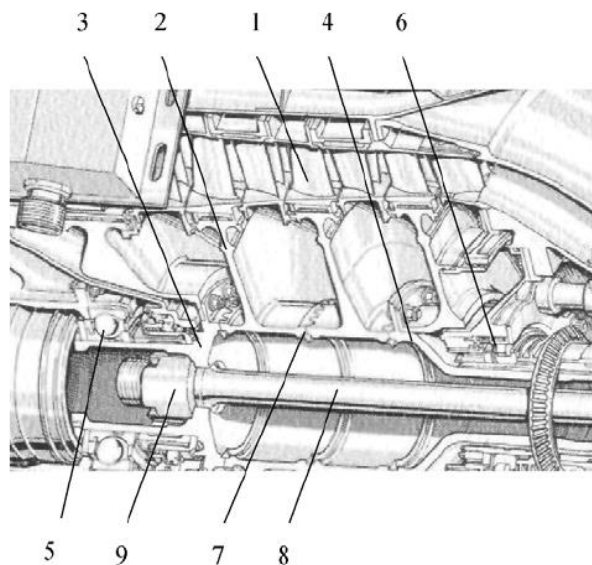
Ротор компресора двигуна Honeywell TFE731-60
